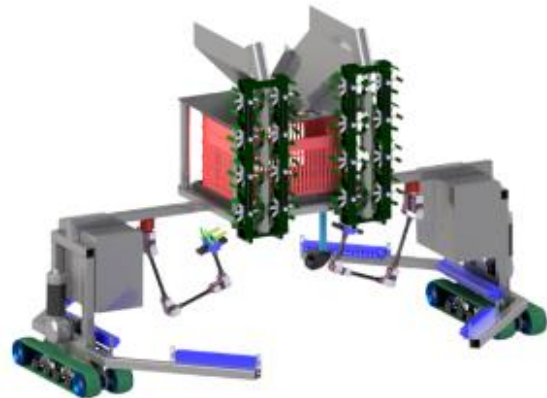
Diseño mecánico de la máquina cosechadora de espárragos.
